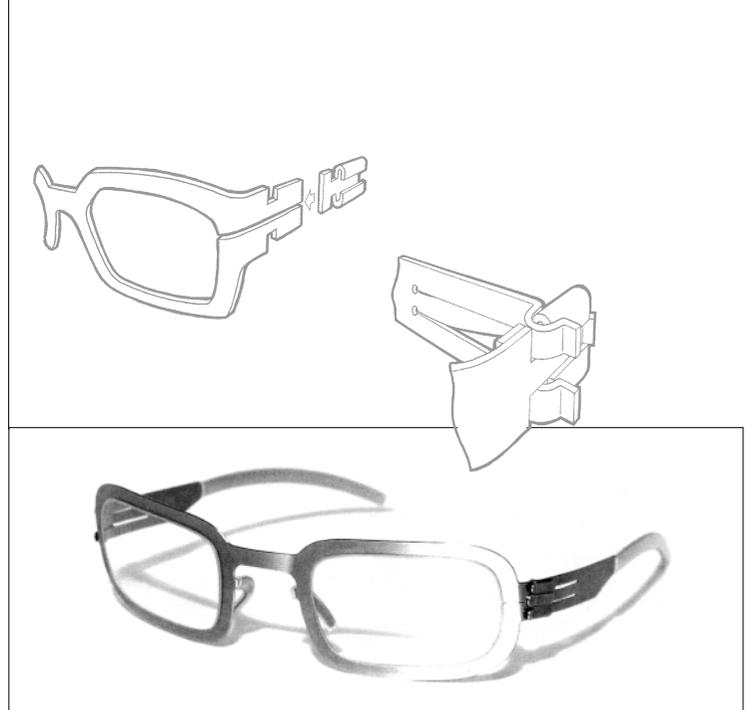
So wie die NewCraft Möbel aus Holzplatten gefräst sind, wird diese Brille mit dem Laserstrahl aus Edelstahl-Blech gefertigt – rentabel auch in kleineren Stückzahlen
